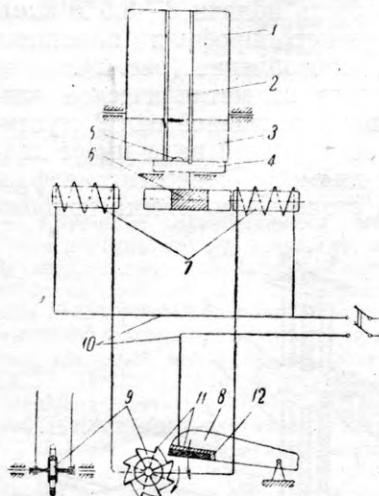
Кинематическая схема механизма наборки и подачи гвоздей:
